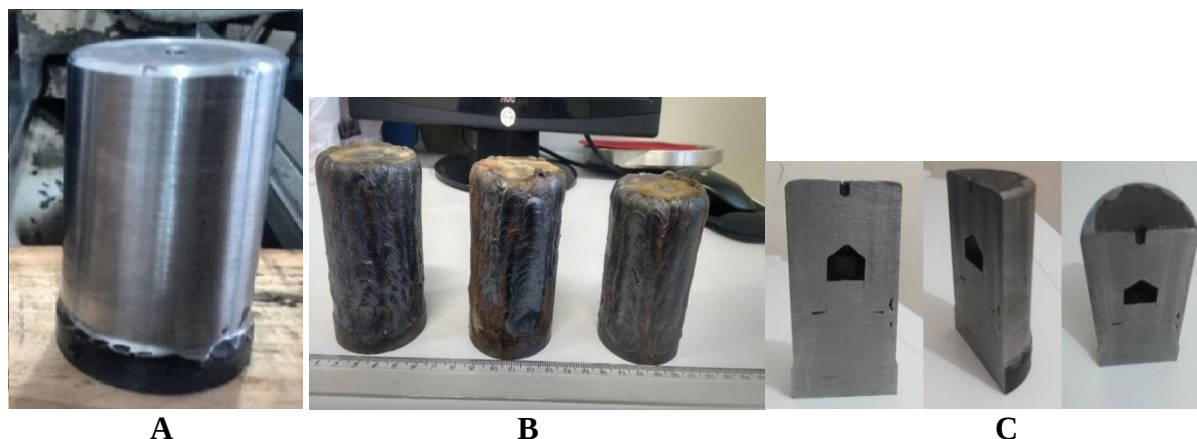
Eixo simulado antes do processo de soldagem (A), após a soldagem (B) e corte transversal após a usinagem às dimensões desejadas (C).
